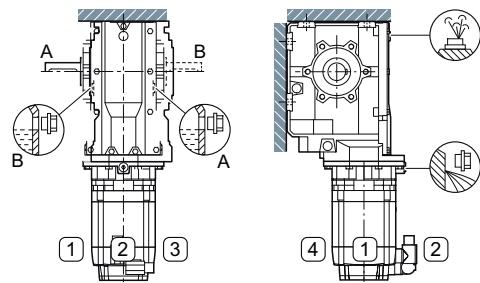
Einbaulagen für Servo-Kegelradgetriebemotor B, Fußausführung, Baugrößen 19 - 29, 2-stufig
